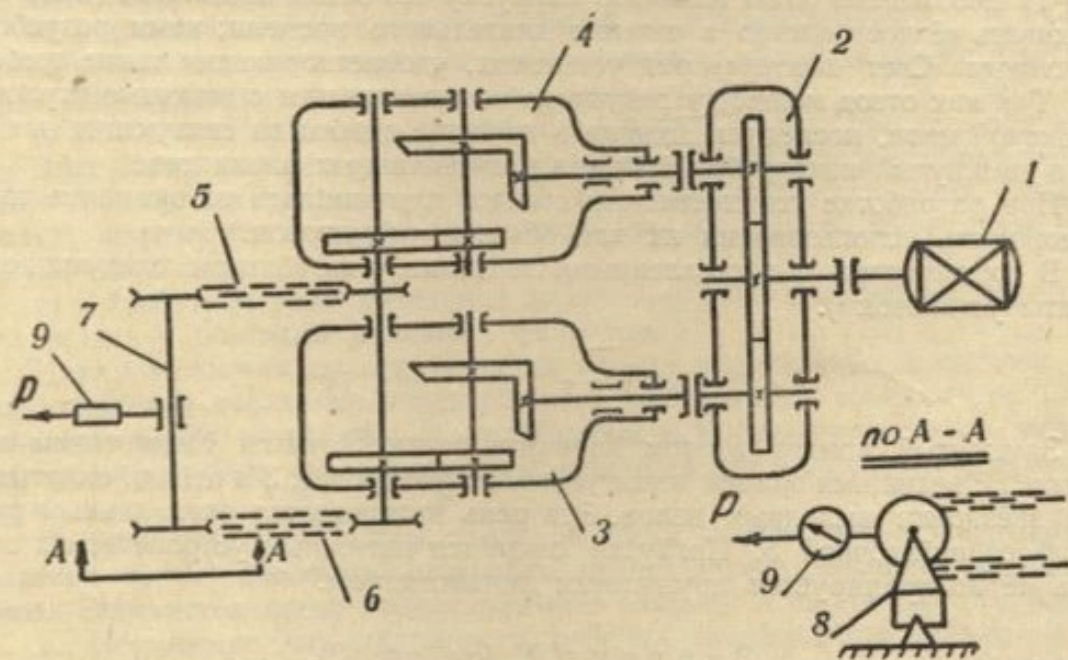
1 — Электродвигатель, 2 — цилиндрический редуктор, 3, 4 — испытуемые редукторы, 5, 6 — втулочно-роликовая цепь, 7 — промежуточный вал, 8 — качающаяся опора, 9 — динамометр.
